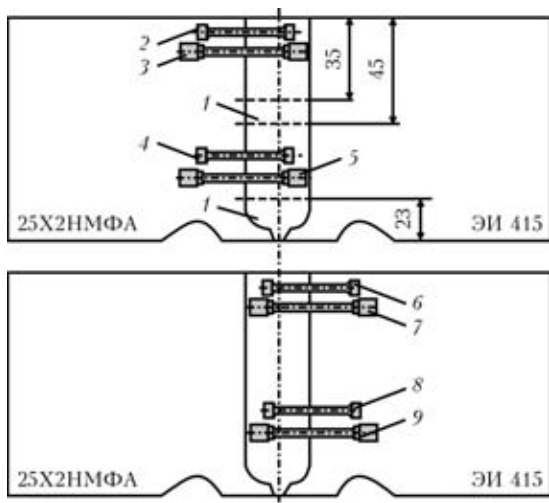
Расположение зон шва по высоте поперечного сечения комбинированного сварного соединения и схема вырезки образцов для испытания на растяжение (обозначения см. в тексте)
